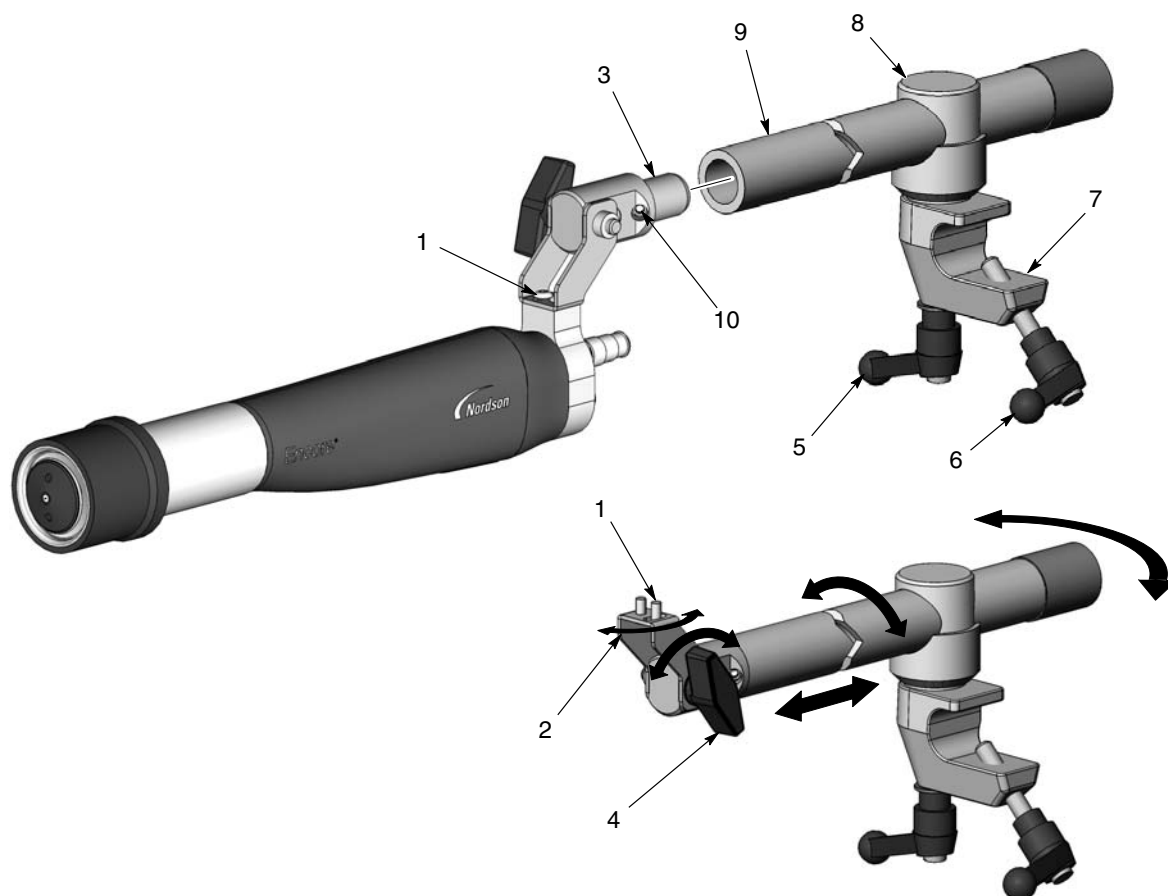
Montaje de la pistola de montaje en barra articulada estándar
